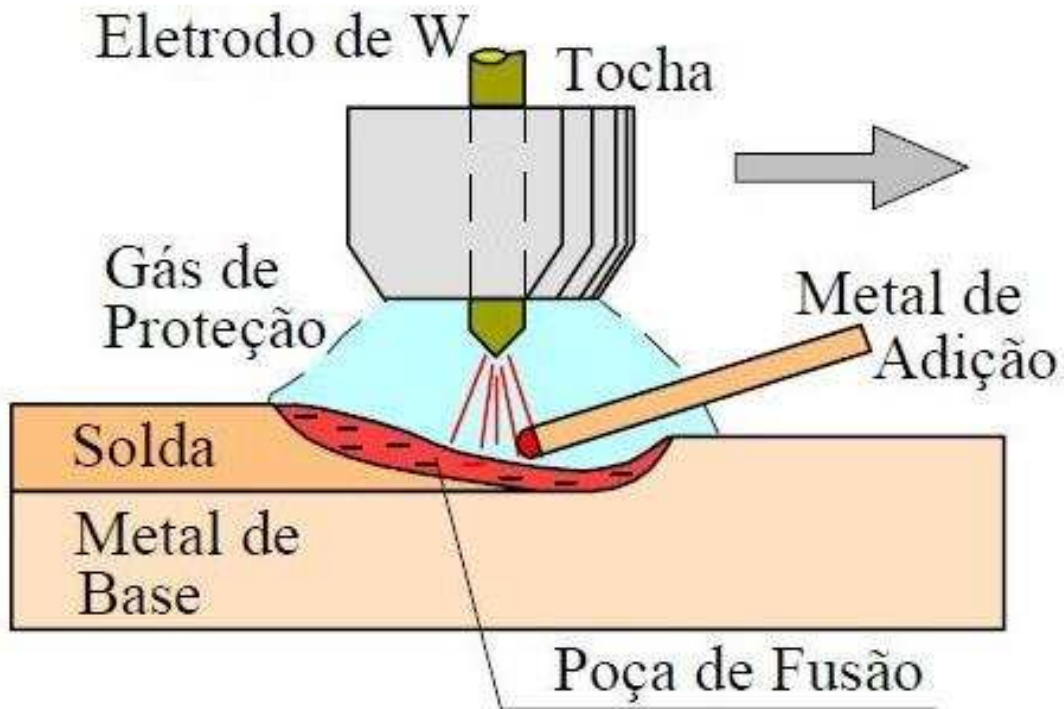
Processo de solda TIG. Fonte: <https://infosolda.com.br/851-trabalho-pratico-tecnica-operatoria-da-soldagem-gtaw/>
